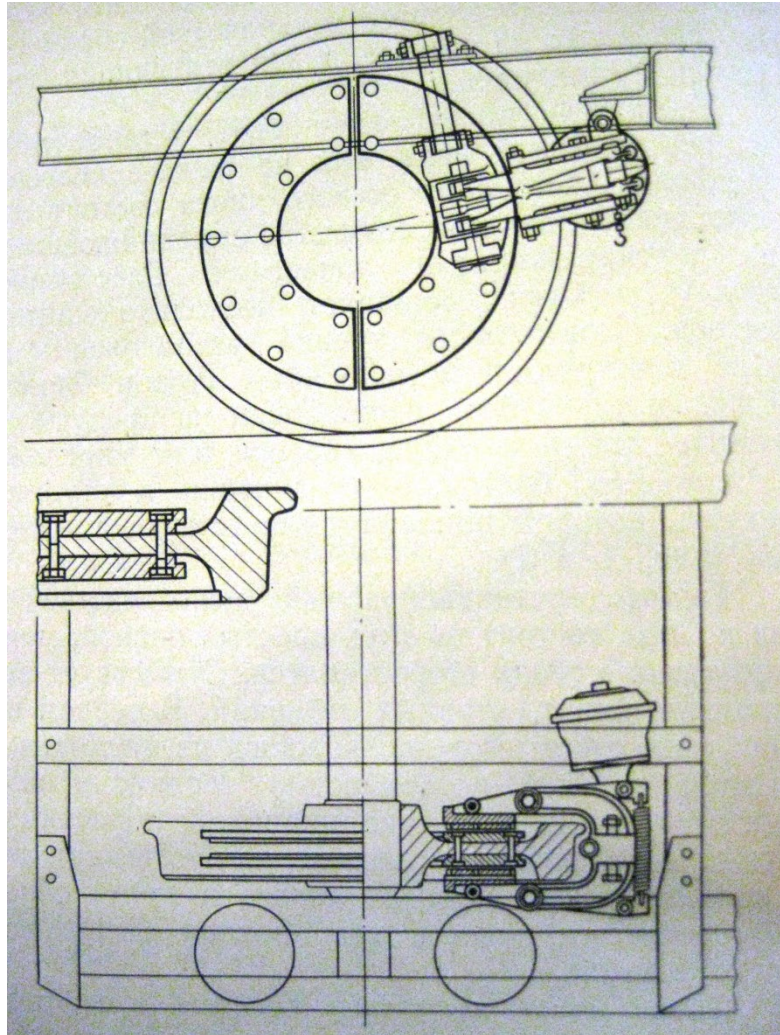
Гальмівний диск, зболчений із центром колеса
